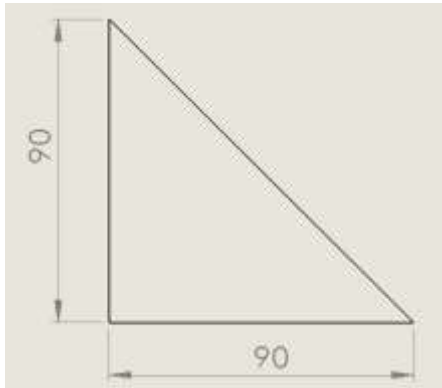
Plano de pieza a fresar mediante función G01. Fuente (El autor).
